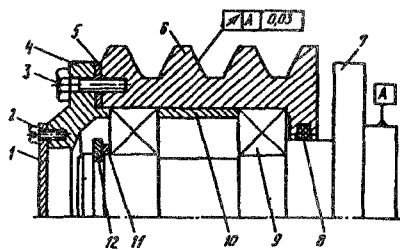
Эскиз ступицы в сборе: 1 — крышка; 2,3 — винты; 4 — фланец; 5 — прокладка; 6 — шкив; 7 — ступица; 8 — кольцо уплотнительное; 9 — подшипник; 10 — втулка; 11 — кольцо компенсационное; 12 — кольцо стопорное
